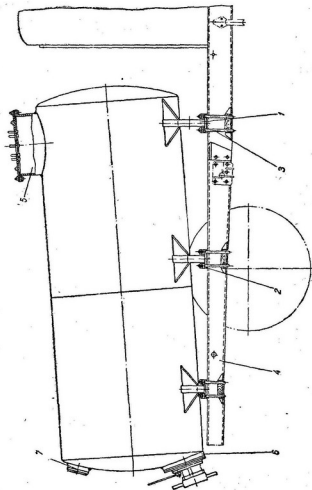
Цистерна: 1 — опорные кронштейны; 2 — резиновые прокладки; 3 — стремянки; 4 — балка рамы; 5 — горловина; 6 — фланец лючка; 7 — фланец смотрового окна.
